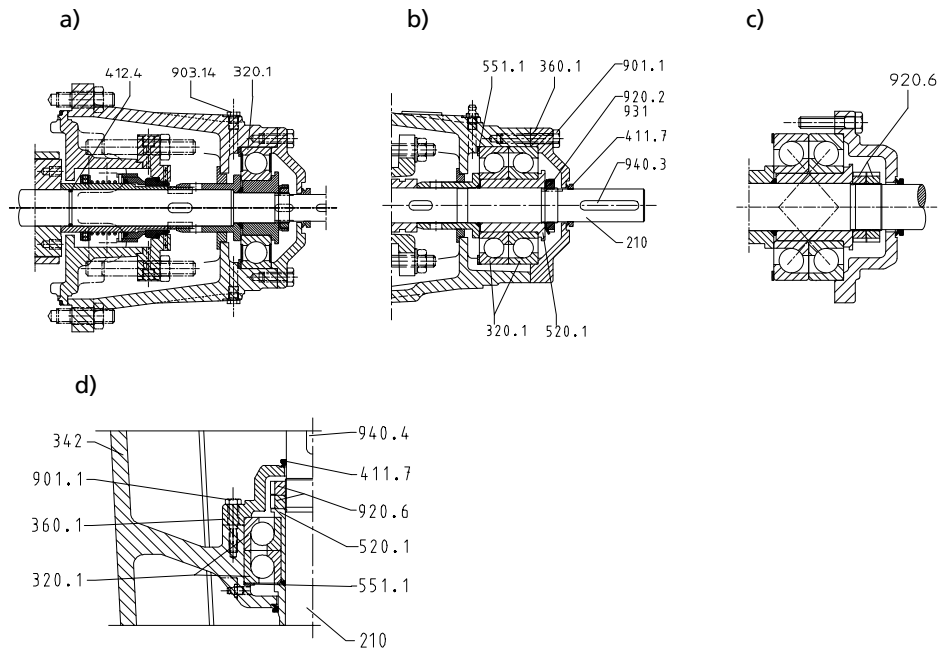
Консистентная смазка: а) типоразмер 32 и б) типоразмер 50-65 и с) типоразмер 100-150 и d) компоновка V при компоновке 100-150
